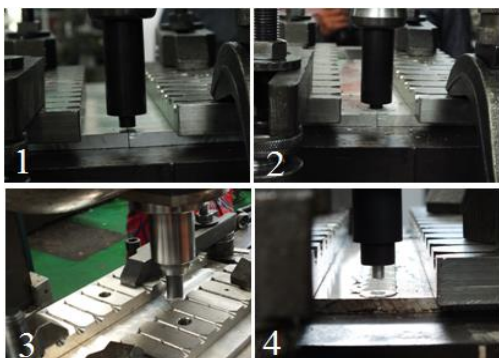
Bentuk Tool Friction Stir Welding
